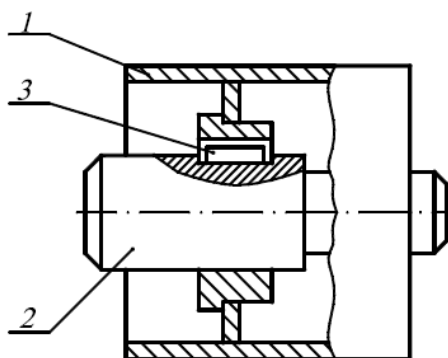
Изображение сварной сборочной единицы на сборочном чертеже.
